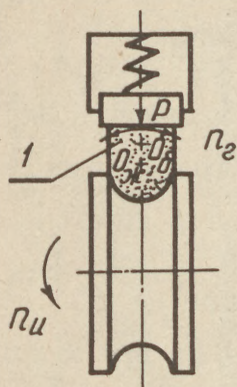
Классическая схема доводки дорожек качения колец шарикоподшипников
